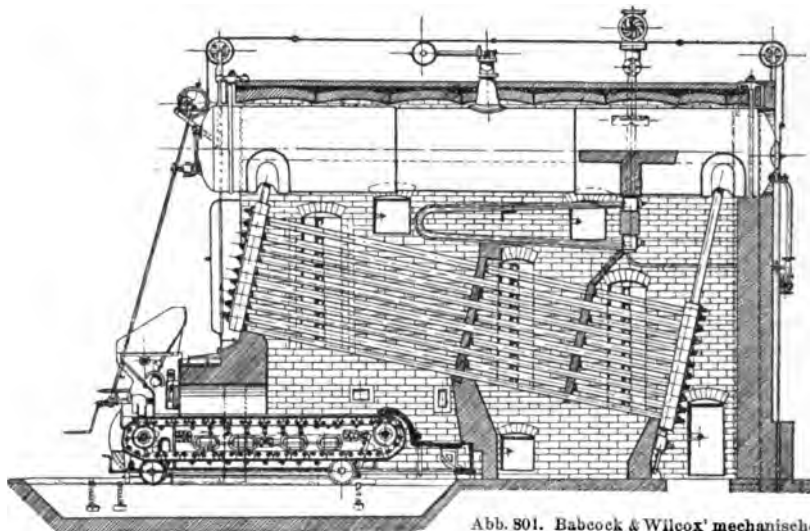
Babcock & Wilcox' mechanische Patentkettenrostfeuerung.
